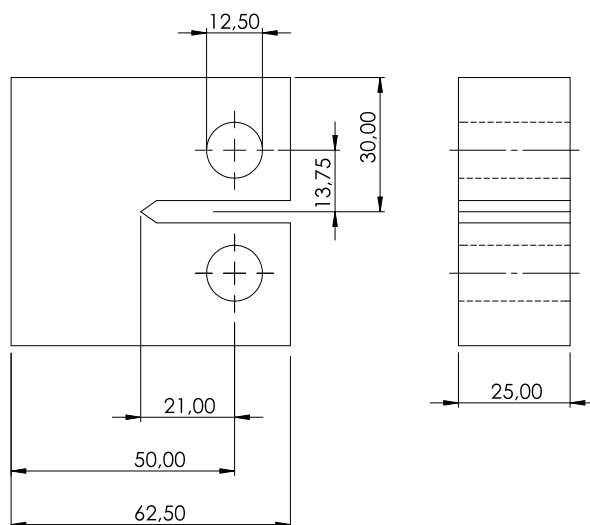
Vistas de alzado y planta de la probeta Compact acotadas.
